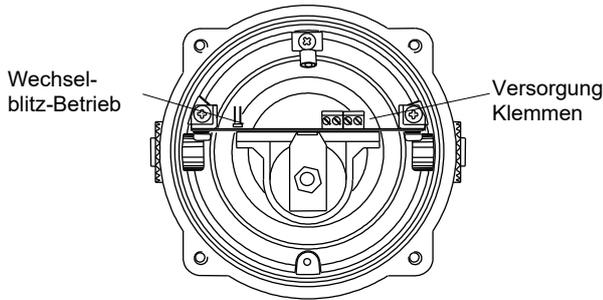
Innenansicht der Joule-Leuchten BExBG10D und BExBG15DD
